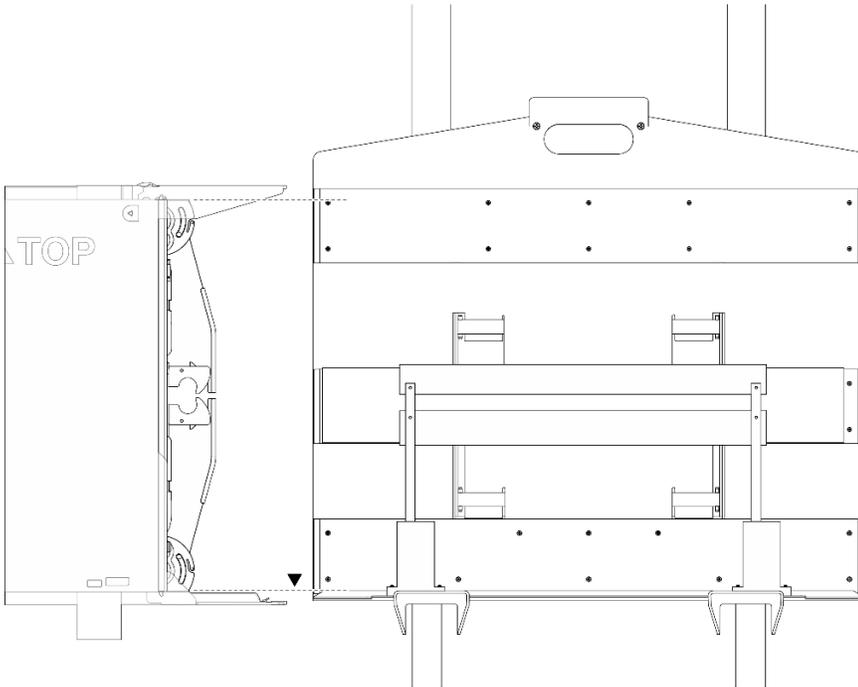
Aligement de la face avant du dispositif sur la face arrière du plateau
